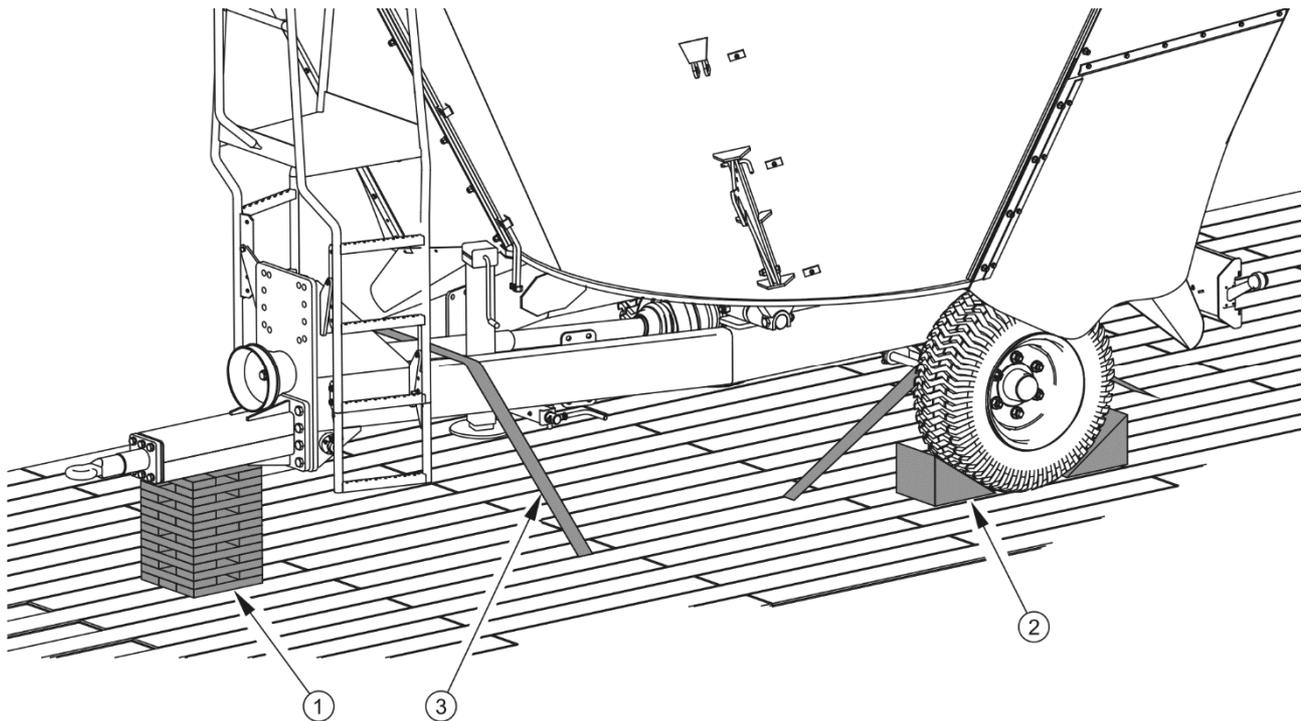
Exemple d'un plan d'amarrage du char mélangeur
